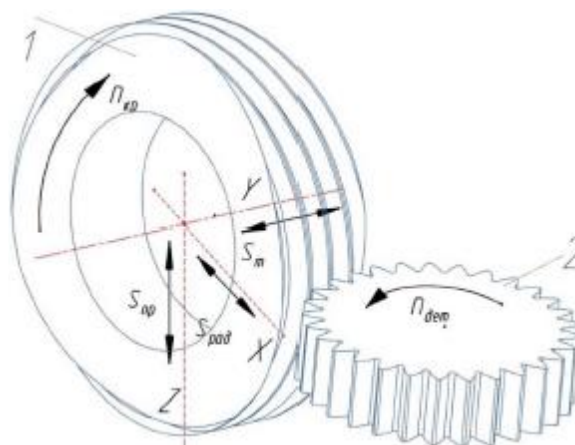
Схема обкатного безперервного зубошліфування: 1 – черв'ячне коло; 2 – зубчасте колесо
